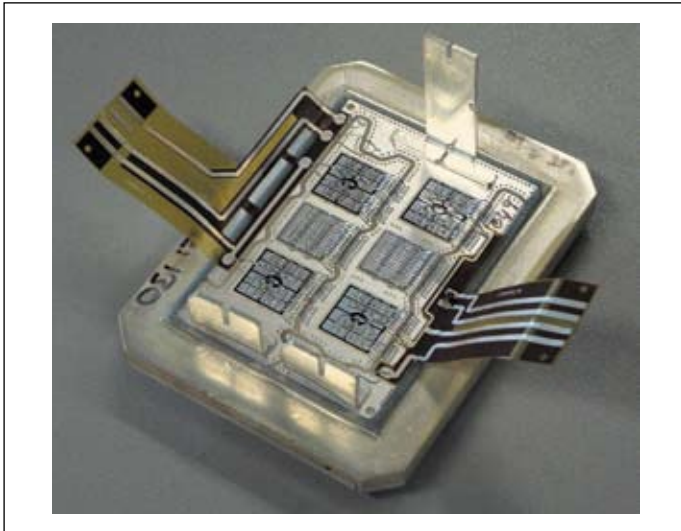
«Референтный» модуль со сварными алюминиевыми проводниками
